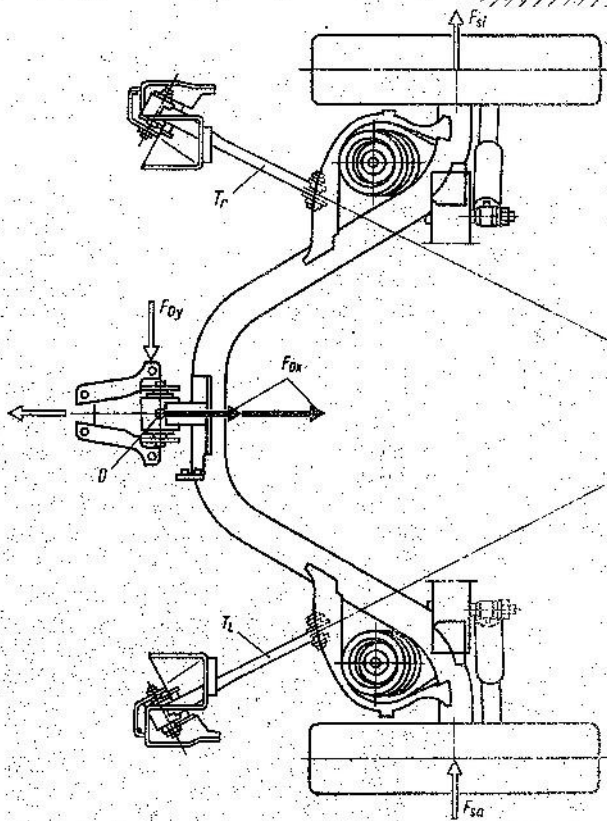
Вид сверху на заднюю подвеску неведущих колес автомобиля «Лянчия-Y10» с косыми штангами, с расположенными перед осью колес и удачным образом широко расставленными пружинами и амортизаторами заднего расположения. Чтобы не заужать погрузочную поверхность, аморти-
